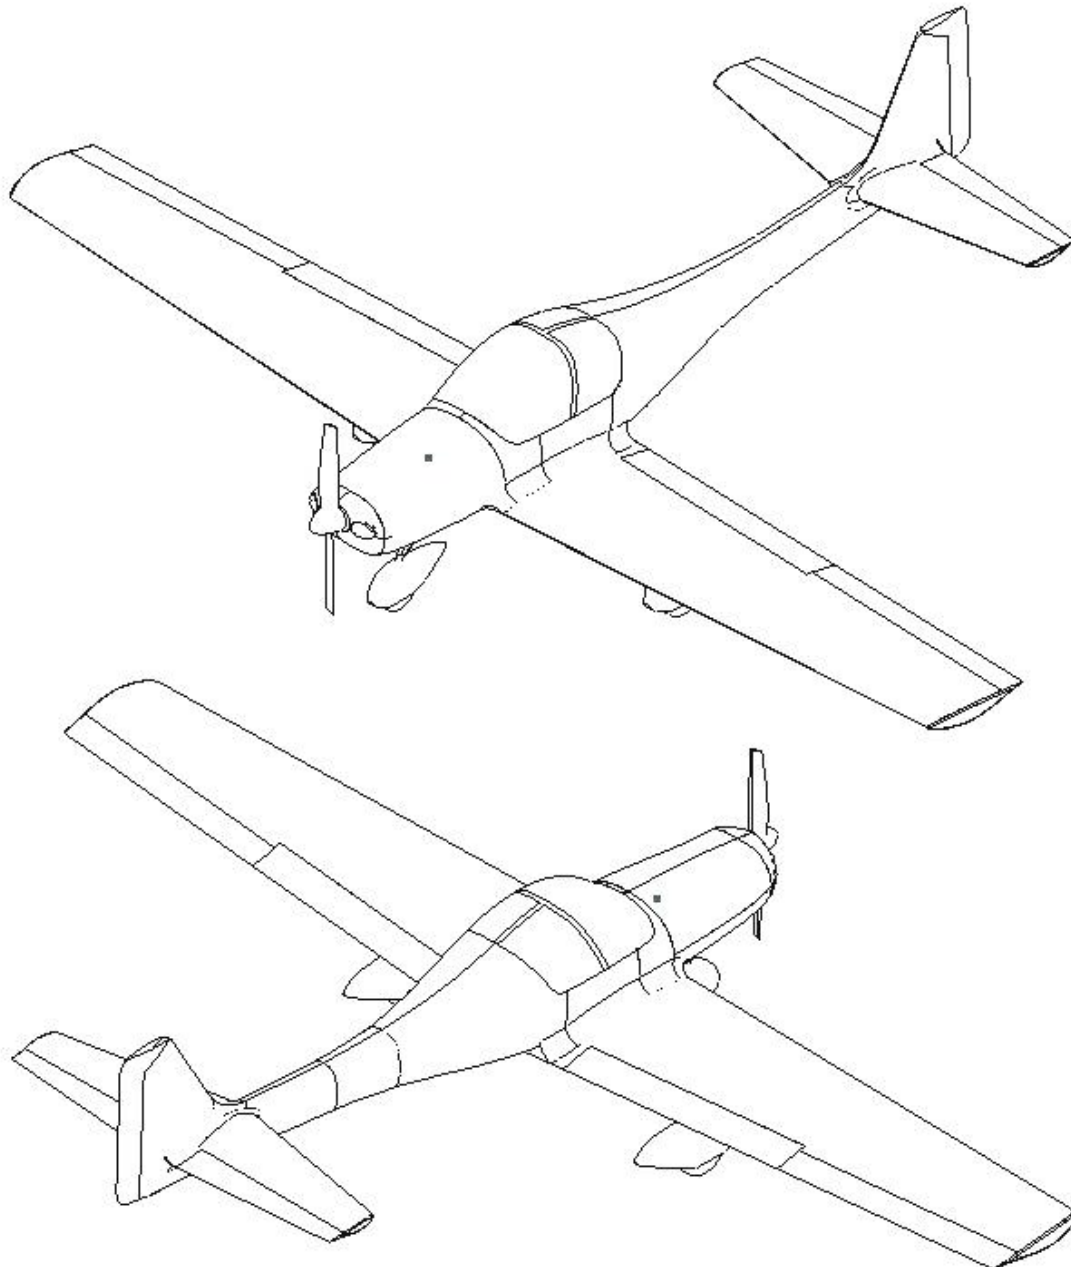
Vistas Isométricas - Desenho Tridimensional
